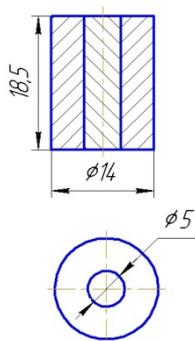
Заготовка под выдавливание компрессорной лопатки
